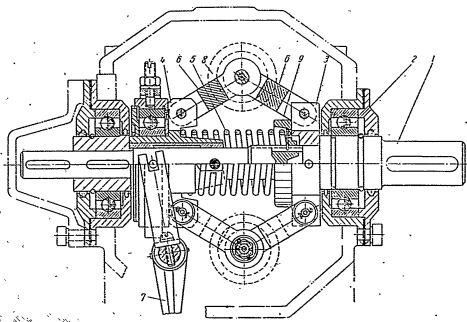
Механизм вращения реле оборотов типов РМН 7011 и РМВ 7011: 1 — вал; 2 — шариковые подшипники; 3 — втулка; 4 — подвижная муфта; 5 — распорная пружина; 6 — рычаг; 7 — рычаг; 8 — добавочные грузы; 9 — регулировочная гайка
